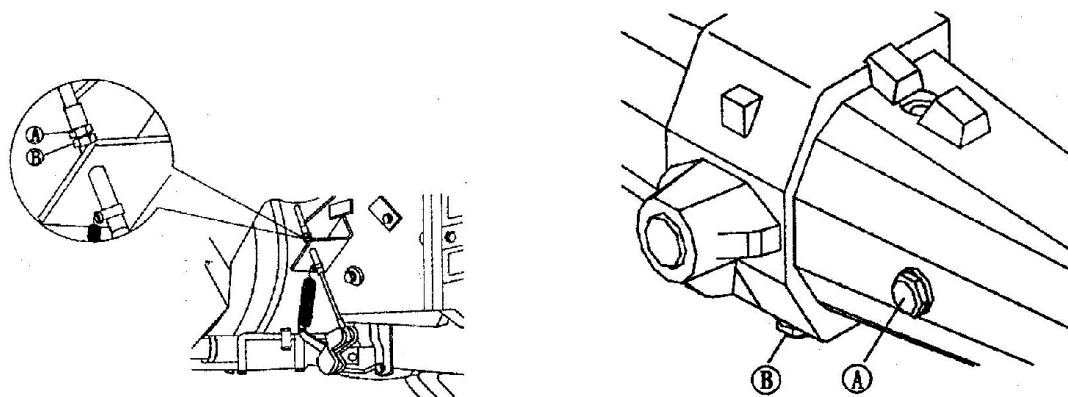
Регулировка стояночного тормоза Рис. 5-26 Проверка уровня масла в корпусе переднего привода
